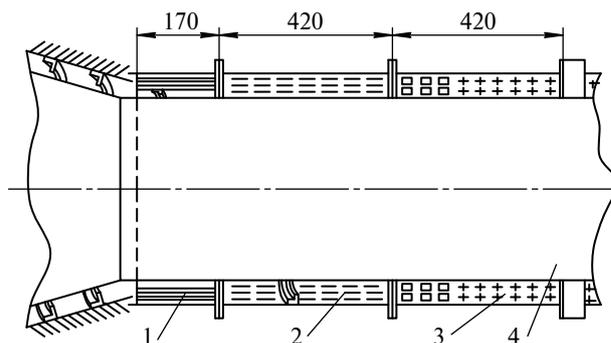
Схема размещения элементов ПСТР-10В: 1 — глухие терочные поверхности; 2 — решетки с терочными поверхностями; 3 — универсальные терочные поверхности; 4 — ротор
